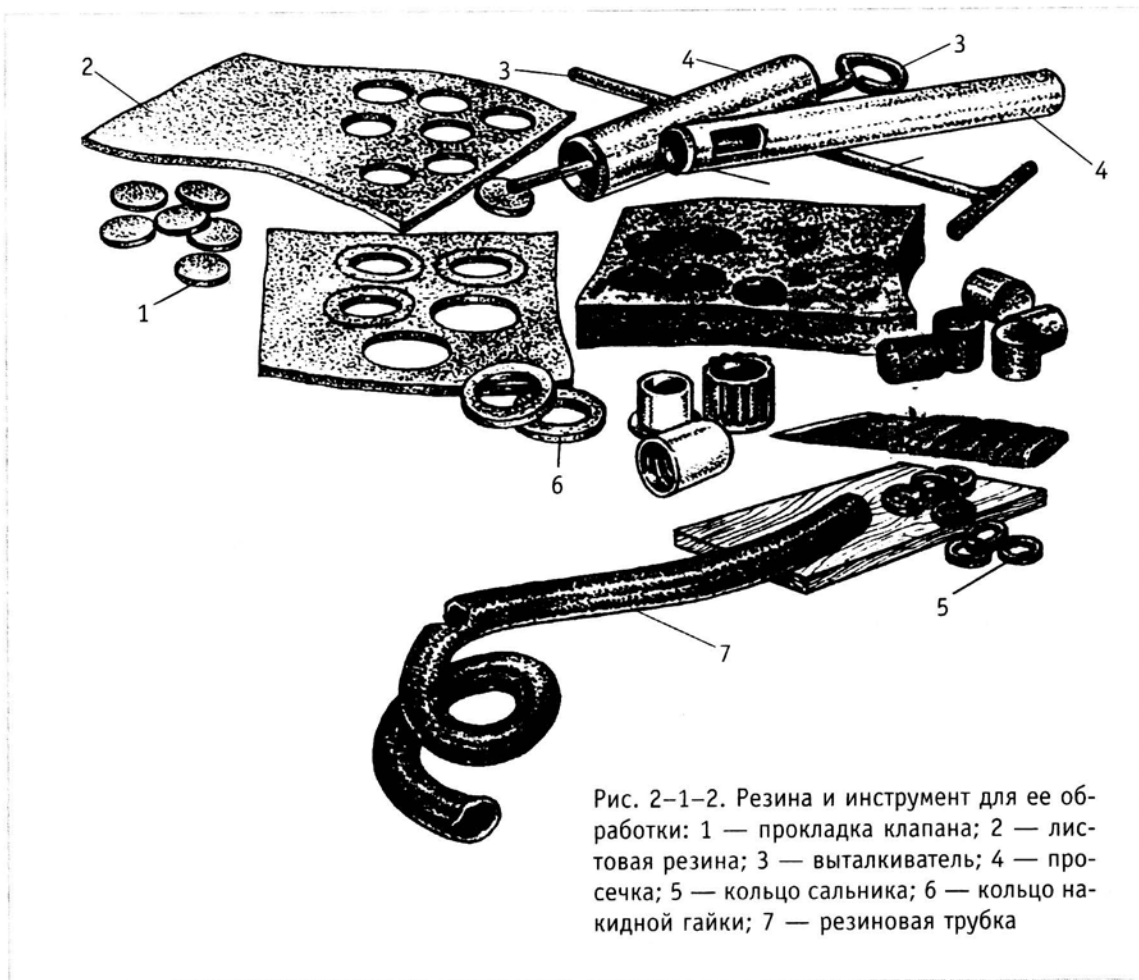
Резина и инструмент для ее обработки: 1 — прокладка клапана; 2 — листовая резина; 3 — выталкиватель; 4 — просечка; 5 — кольцо сальника; 6 — кольцо накидной гайки; 7 — резиновая трубка
